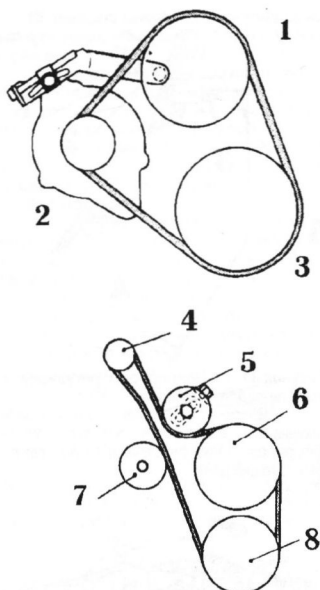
Путь прохождения приводного ремня — сверху изображена типичная ситуация для четырехцилиндрового двигателя; внизу — типичный двигатель V6
